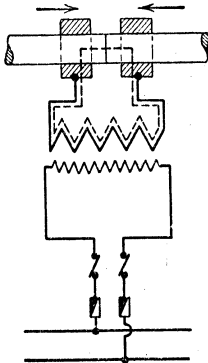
Elektrisches Stumpfschweißen.
